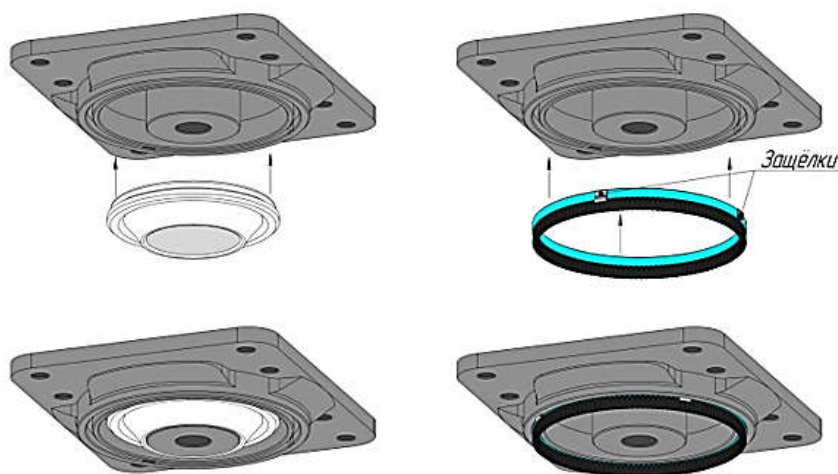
Установка внутреннего кольца подшипника и щётки в пятник
